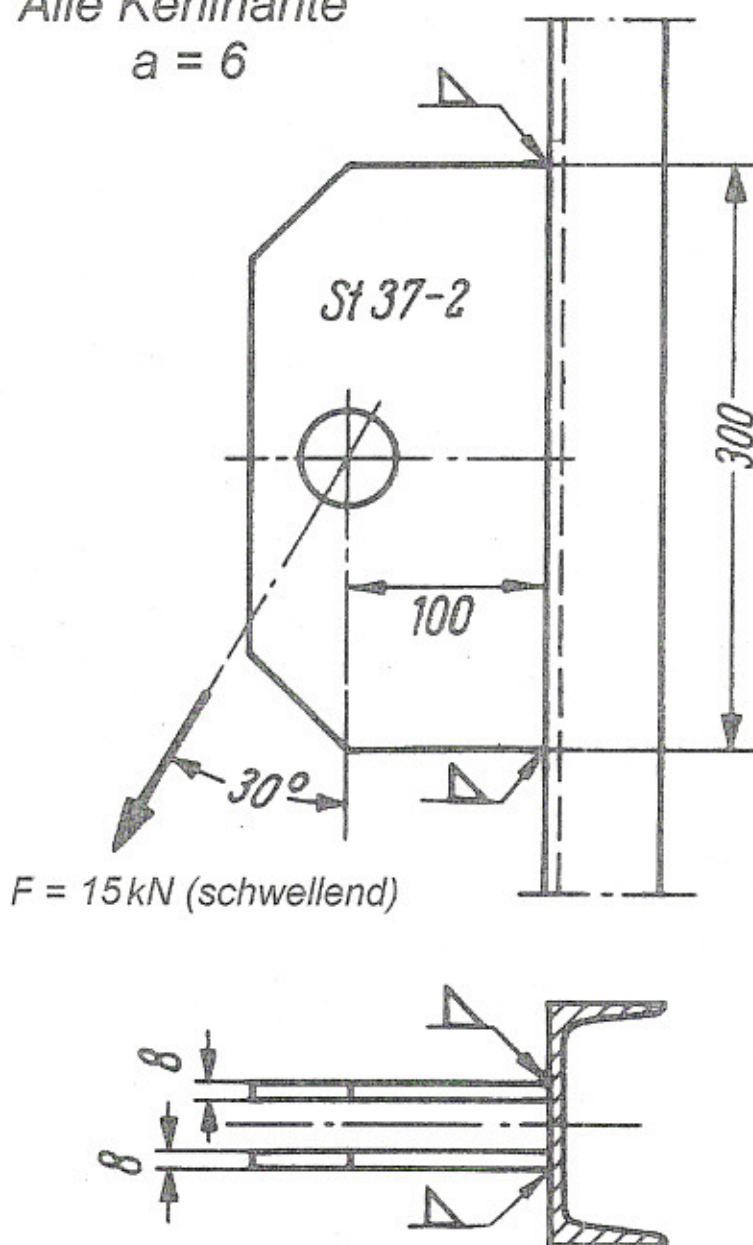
Schweißanschluß für zwei Bleche für eine Seilbefestigung
